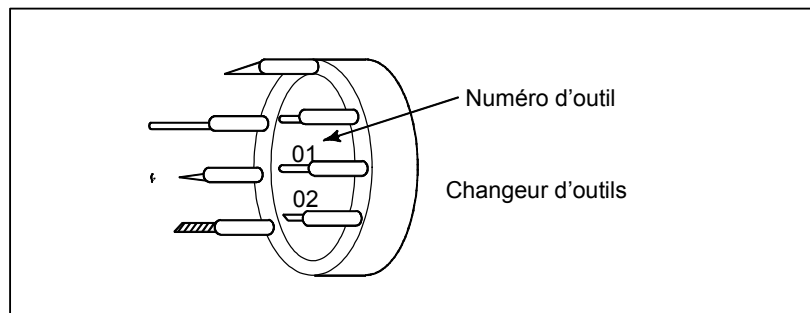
(A) Outil utilisé pour divers types d'usinage
